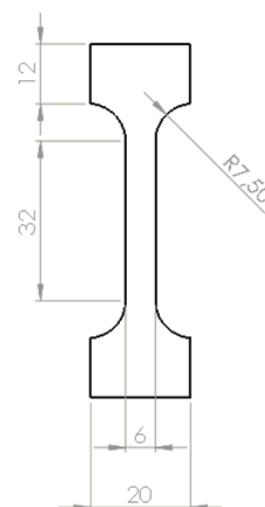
Desenho técnico do provete utilizado na dissertação.
